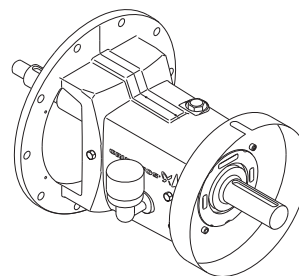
Корпус подшипников с системой постоянного уровня масла
